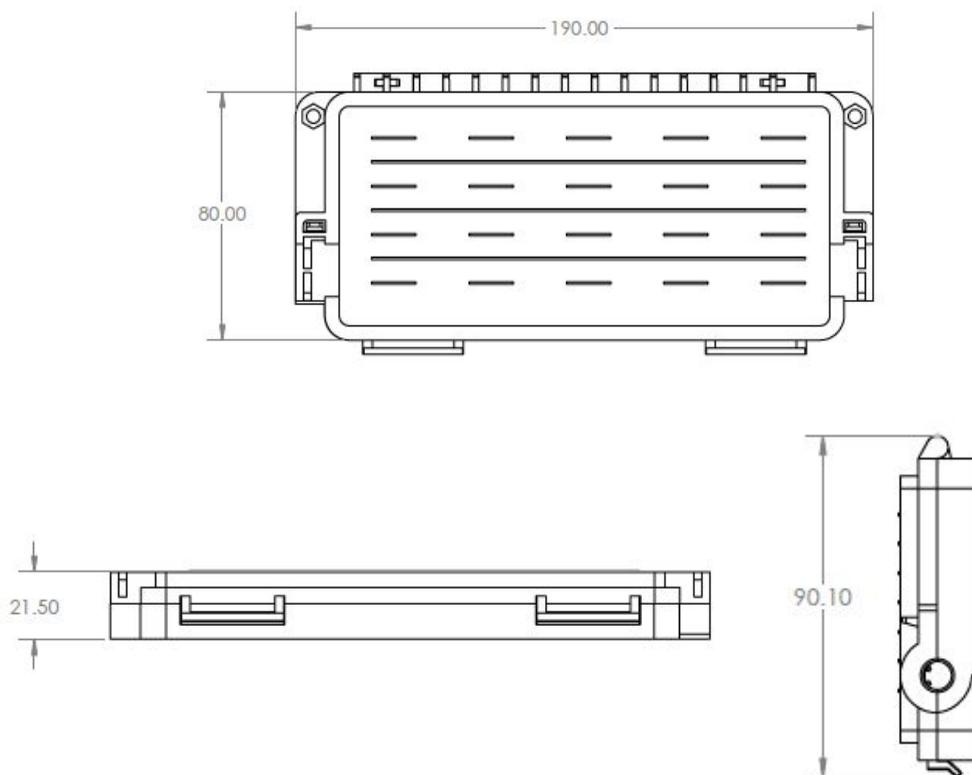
Dimensiones en vista frontal, planta y lateral.
